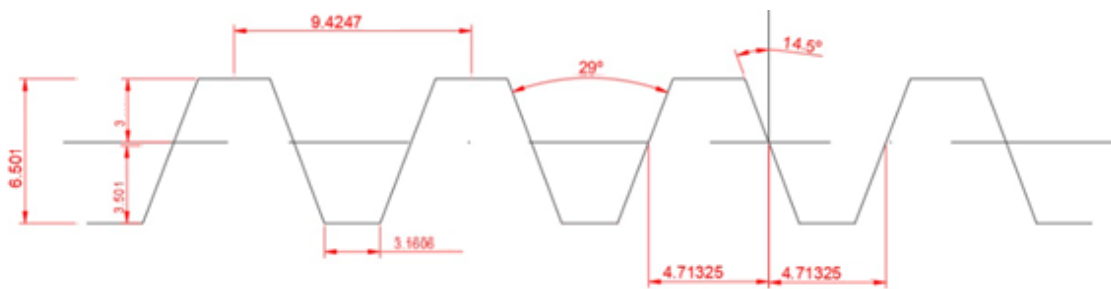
Dimensiones de la rosca del tornillo sin fin.
